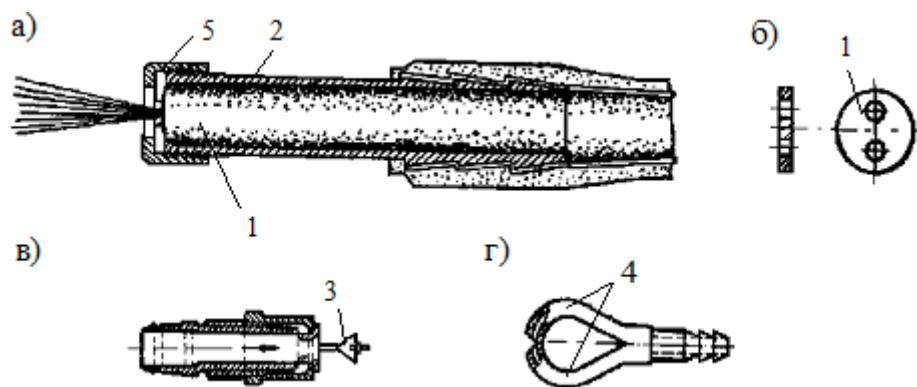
Механическими форсунками: 1 – диафрагма; 2 – корпус; 3 – рассекатель; 4 – трубки; 5 – гайка
